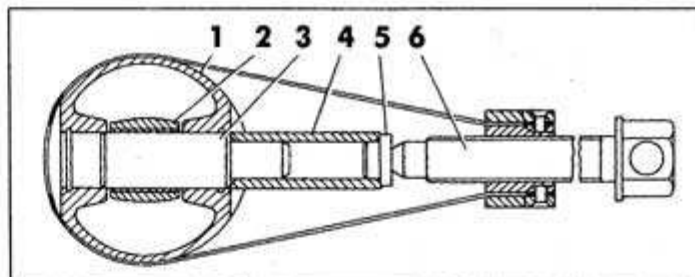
Запрессовка поршневого пальца в поршень и шатун съемником 7823–6102:
